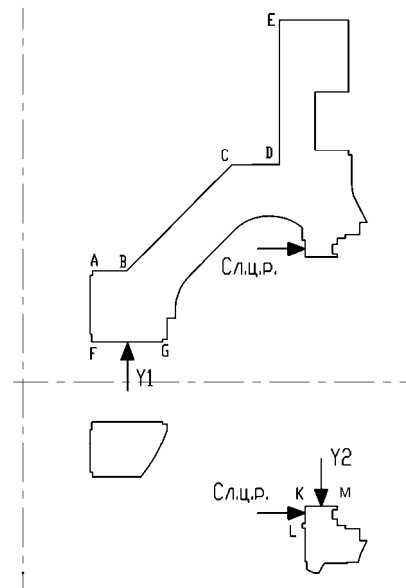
Сечение корпуса РК ПЛ гидротурбины
